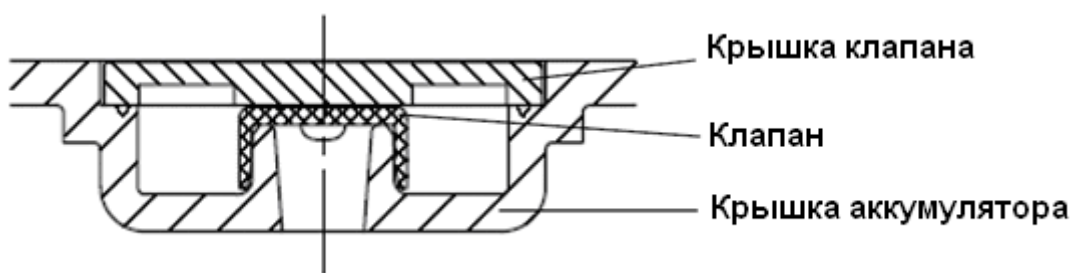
Конструкция клапана Marathon M и Sprinter S
